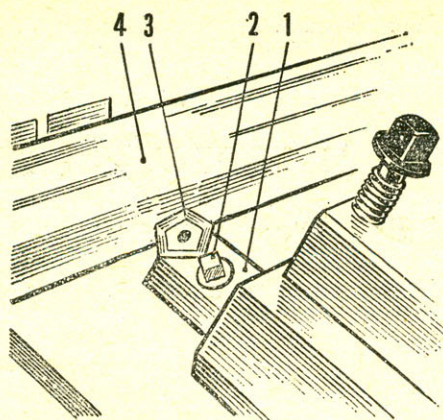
Сборный резец: 1 — державка, 2 — крепежный болт, 3 — твердосплавная режущая пластинка-пятиугольник, 4 — деталь.
